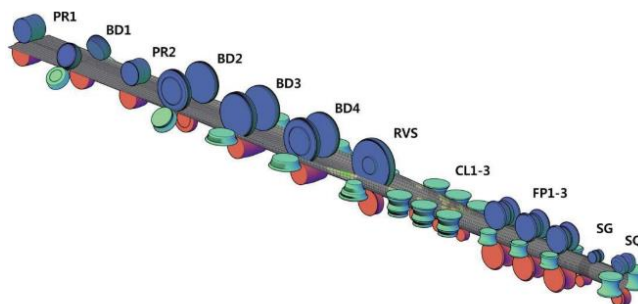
Компоновка оборудования формовочно-сварочного стана ТЭСА 203–530
